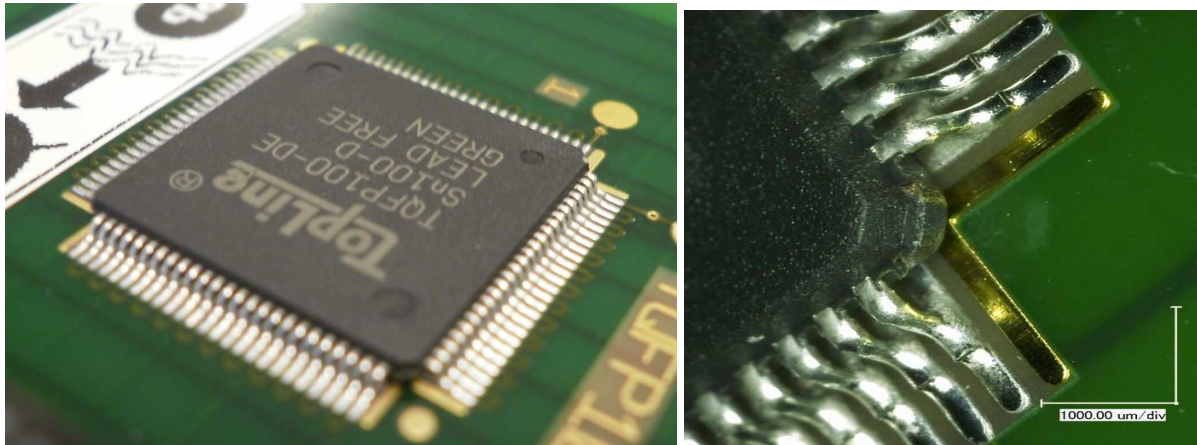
Vue d'ensemble du composant TQFP100 assemblé
